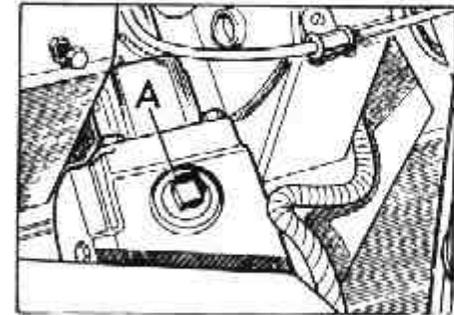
Tapón de llenado de la caja de engranajes de la dirección.
